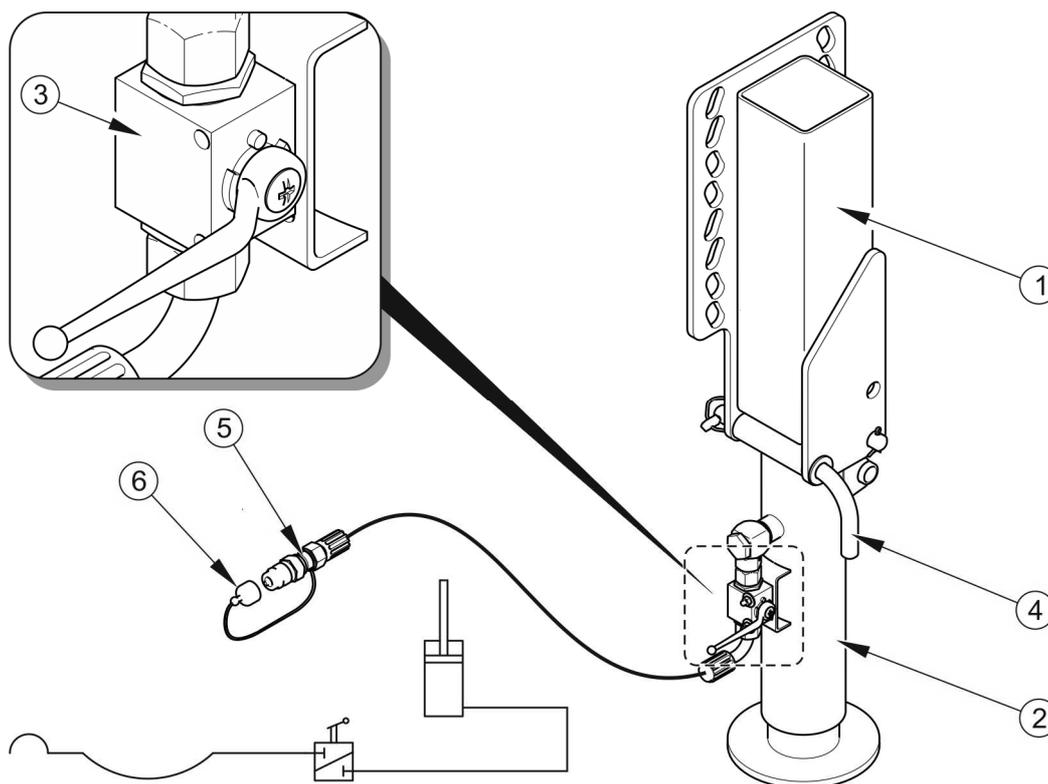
Costruzione e schema dell'impianto idraulico del supporto piegato
